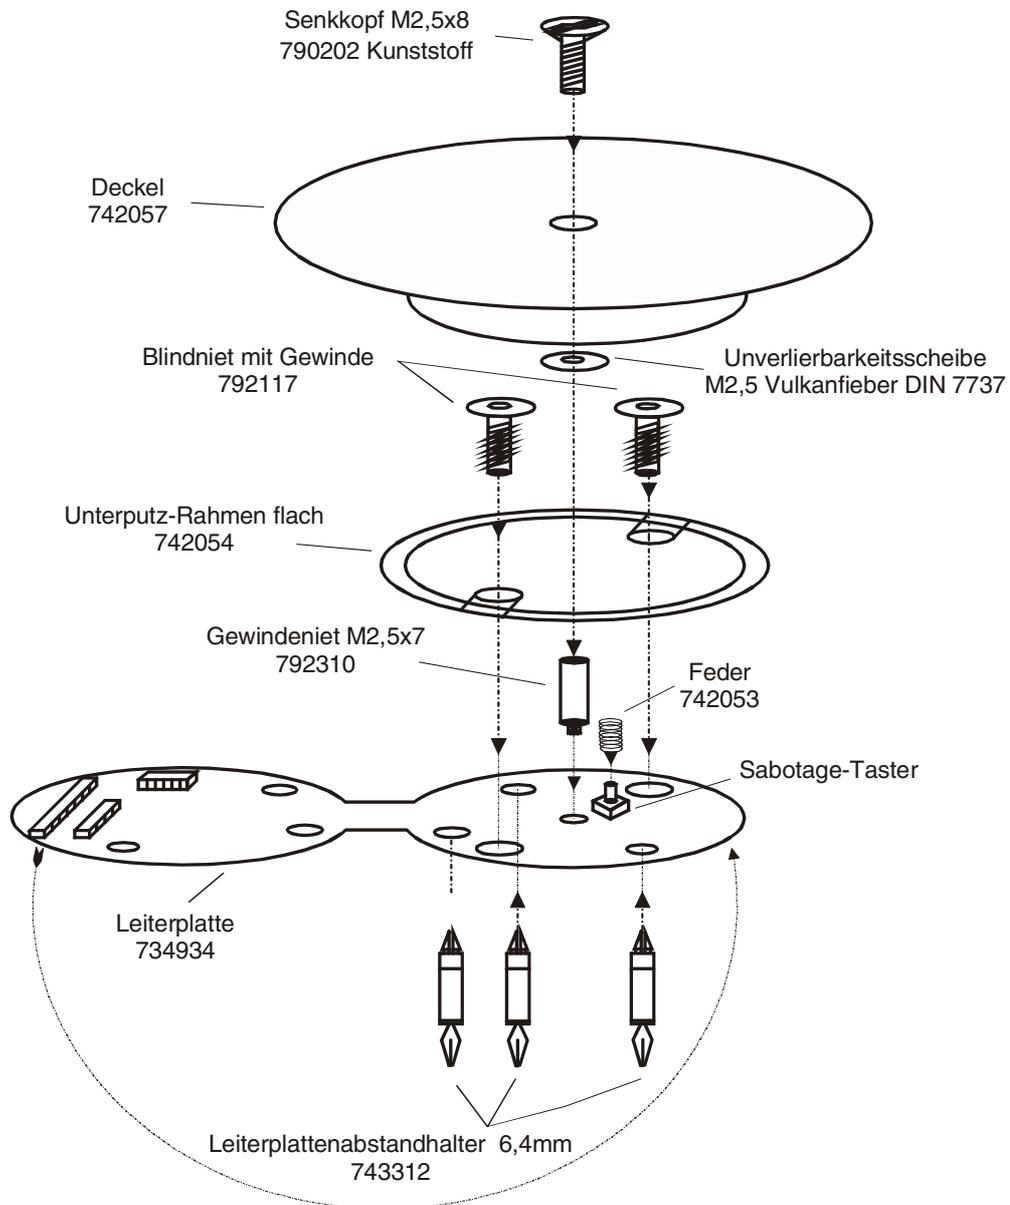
Explosionszeichnung des EMA esserbus® 3 Eingänge/1 Ausgang
